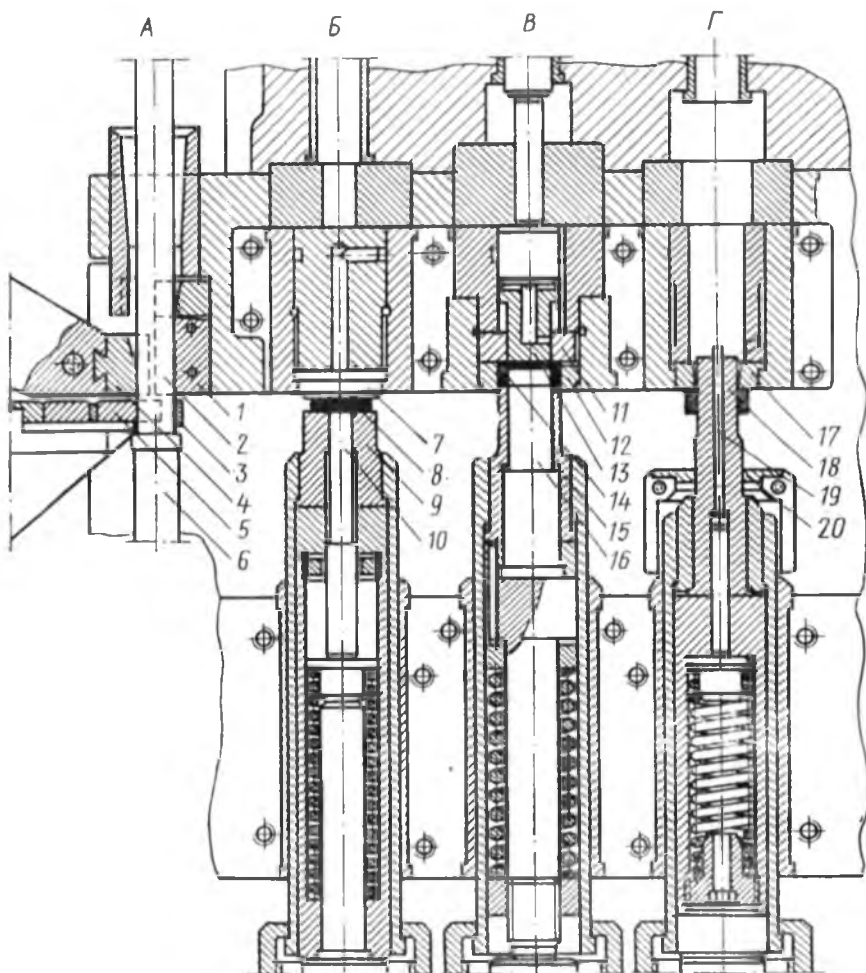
Штамповый инструмент многопозиционного горячештамповочного автомата АМР-30 для изготовления поковок подшипниковых колец и гаек
